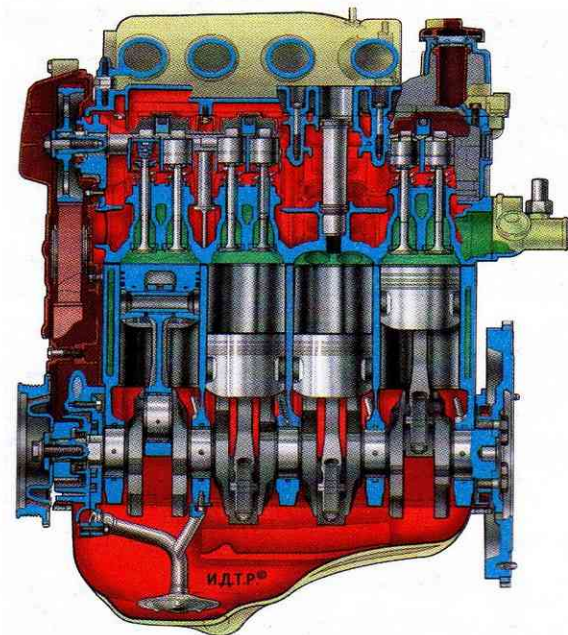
Продольный разрез двигателя ВАЗ-2112
